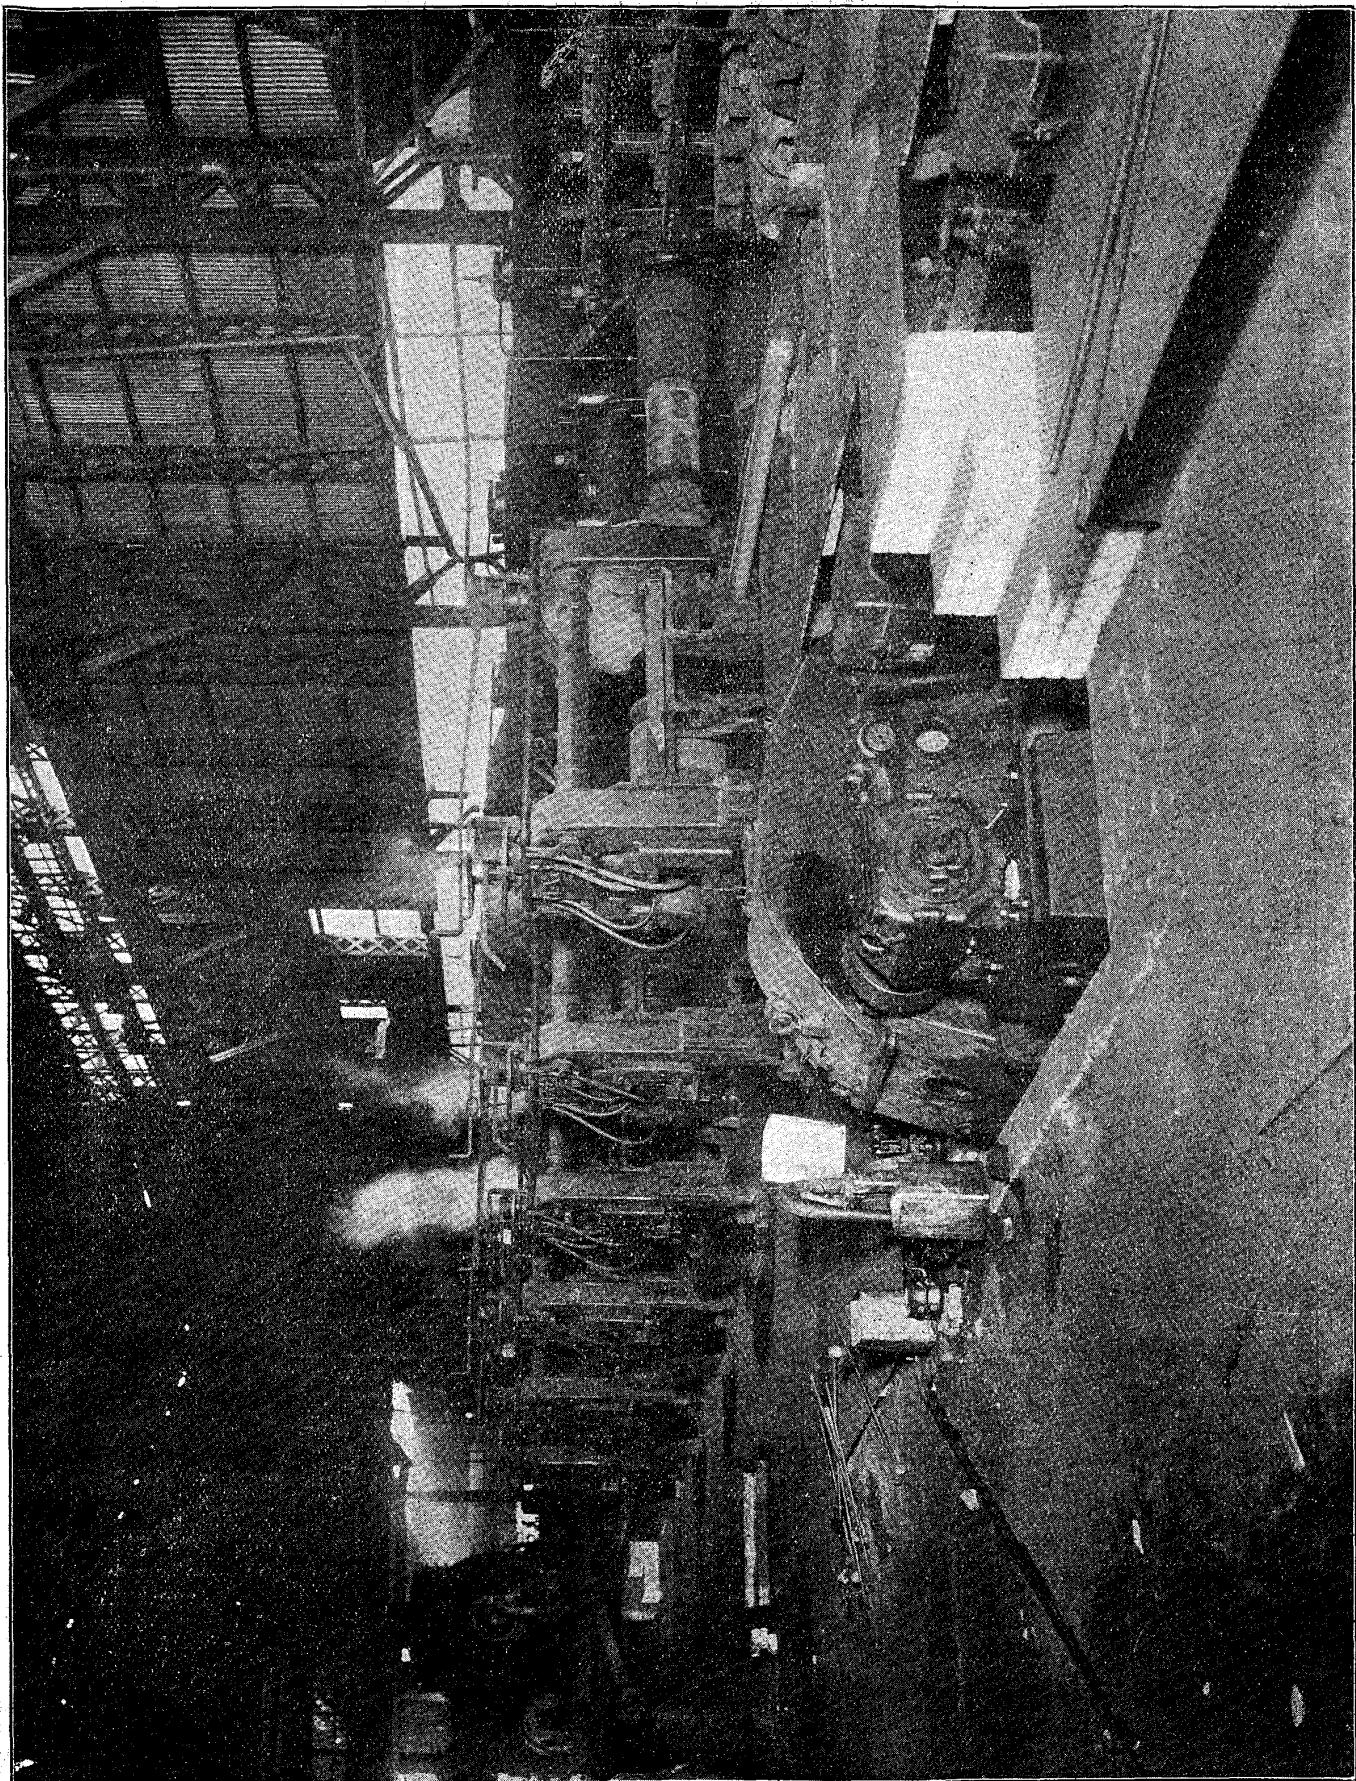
第6分塊工場 第1號連續ロール機 600 mm continuous billet and sheet bar mill
